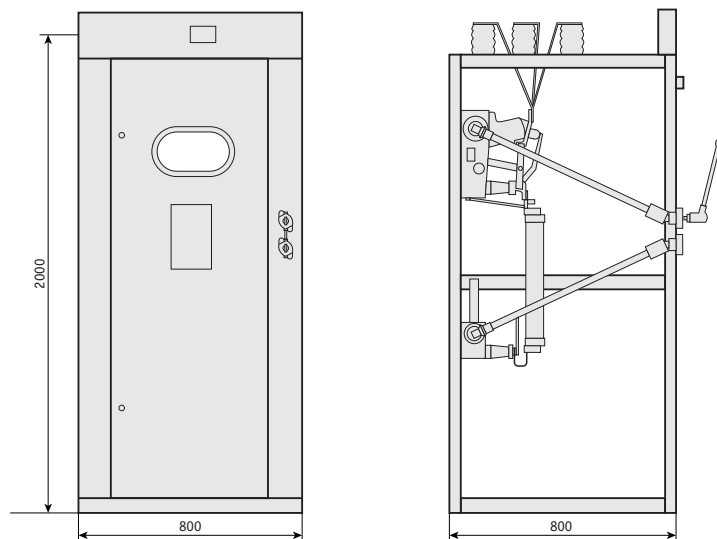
Габаритные и установочные размеры КСО-305 с ОМВ
